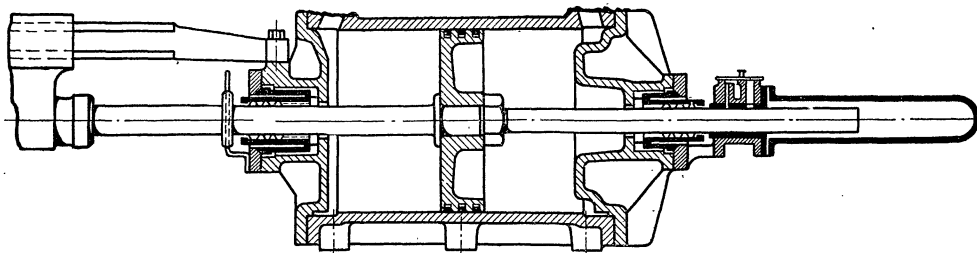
Zylinder mit durchgeführter Kolbenstange.
